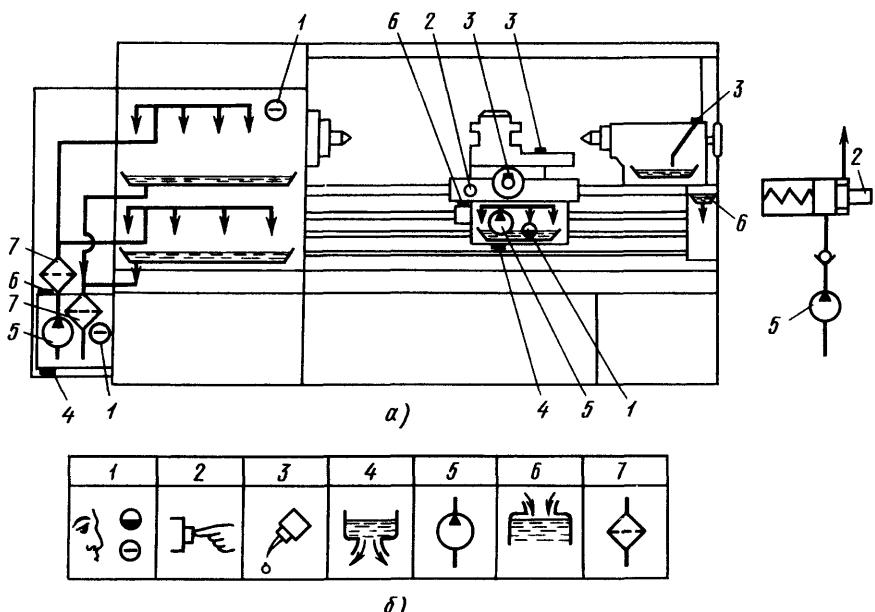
Система смазывания токарно-винторезного станка модели 16К20:
